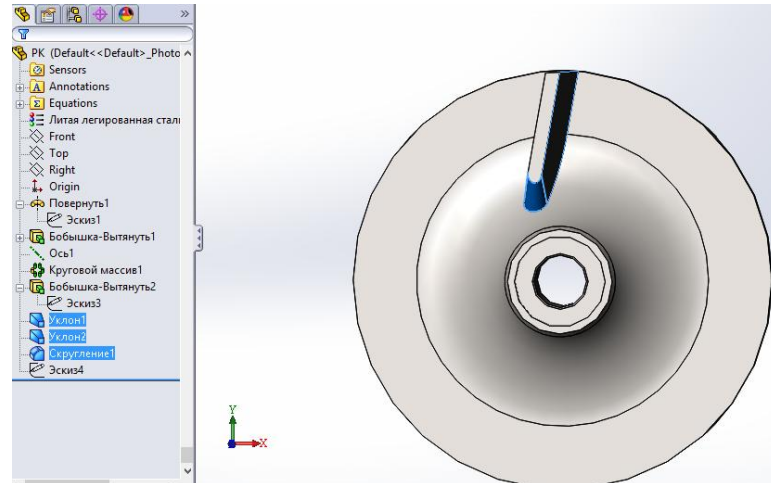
Уточнення конструкції лопаті робочого колеса
